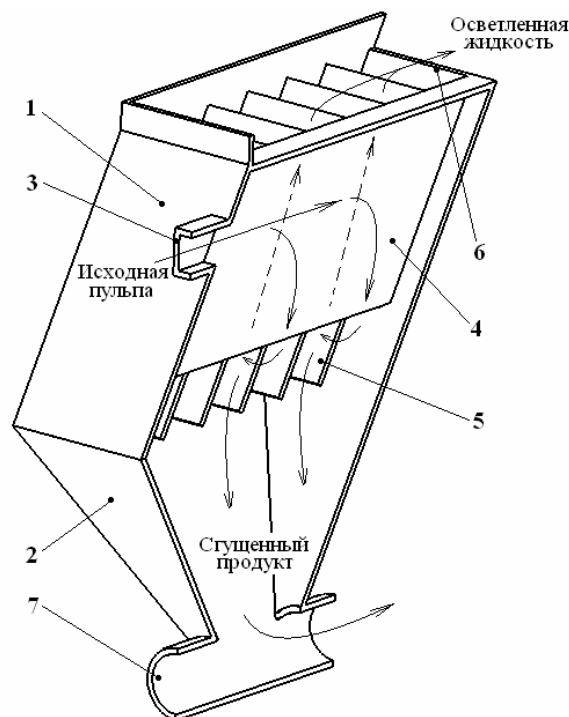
Разрез противоточного пластинчатого сгустителя по плоскости симметрии: 1 – осадительная камера; 2 – разгрузочная камера; 3 – входной патрубок; 4 – центральная стенка; 5 – осадительная пластина; 6 – сливной порог; 7 – труба разгрузочного шнека
